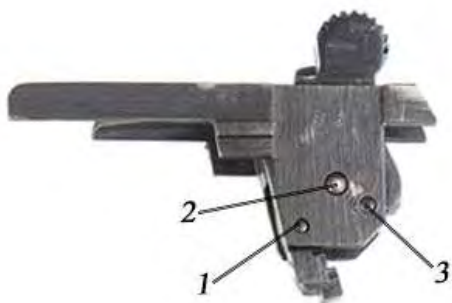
Колодка: 1 – ось шептала; 2 – ось курка; 3 – штифт для упора боевой пружины
